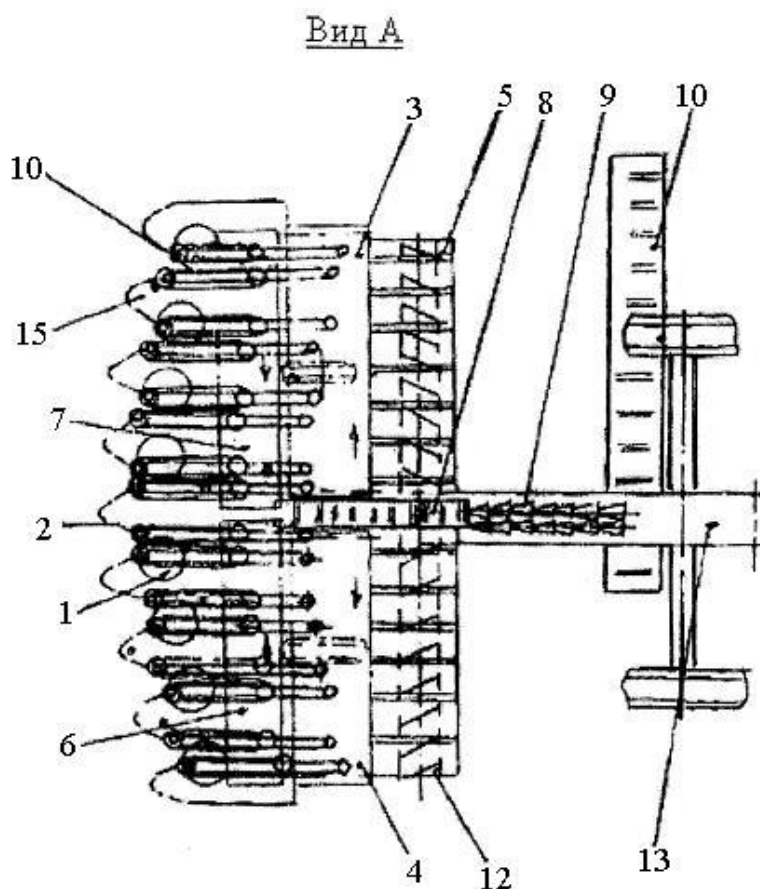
Кукурузоуборочный комбайн с предлагаемыми початкоотделяющими модулями, вид сверху по стрелке А
